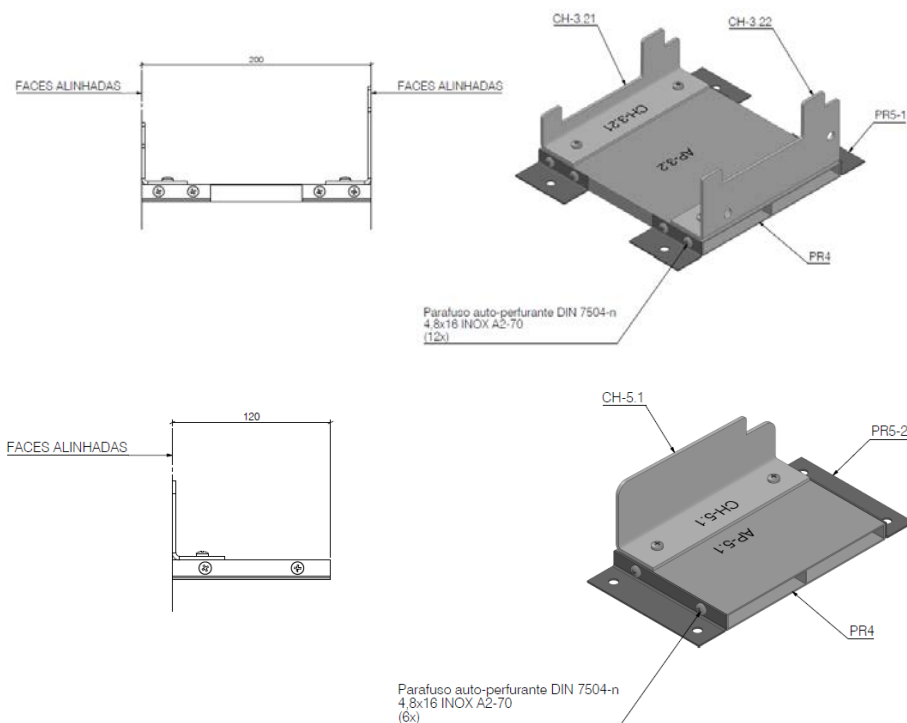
Pormenores construtivos exemplificativos da subestrutura do sistema de revestimento da pala da estrutura ENGAWA.
